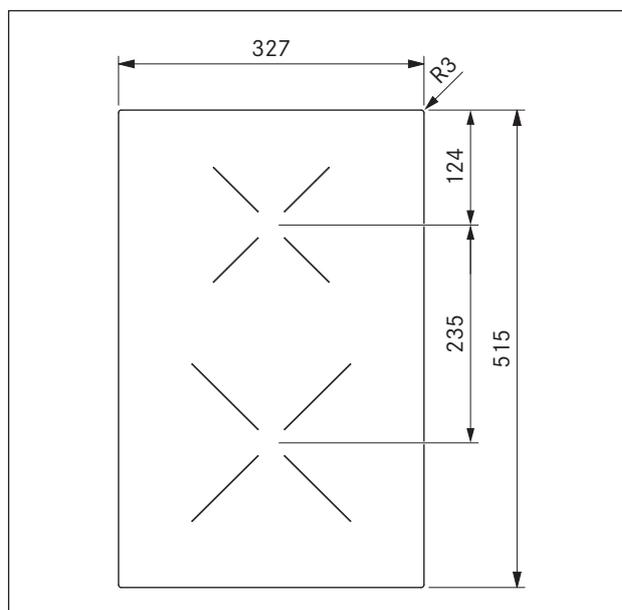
Dimensões do aparelho CKI, vista de cima
